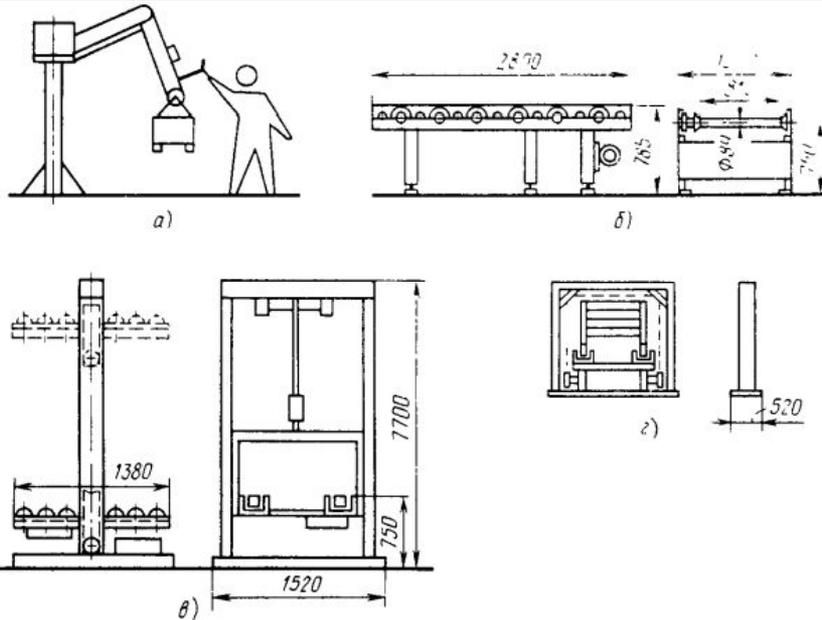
Оборудование для приема и переработки грузов на складах:
